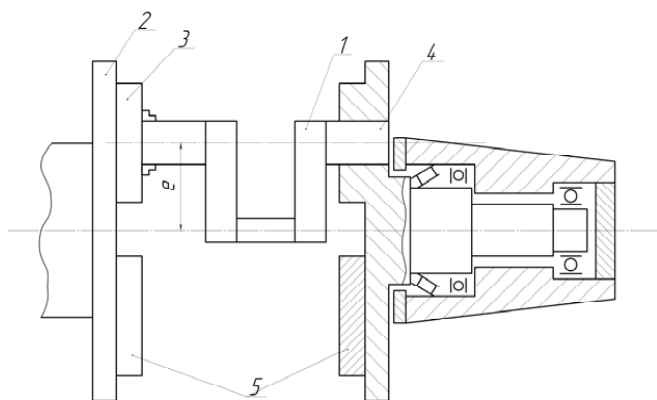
Центросместители для механической обработки коленчатого вала: 1 – вал; 2 – планшайба; 3 – патрон; 4 – планшайба задней бабки; 5 – противовесы
